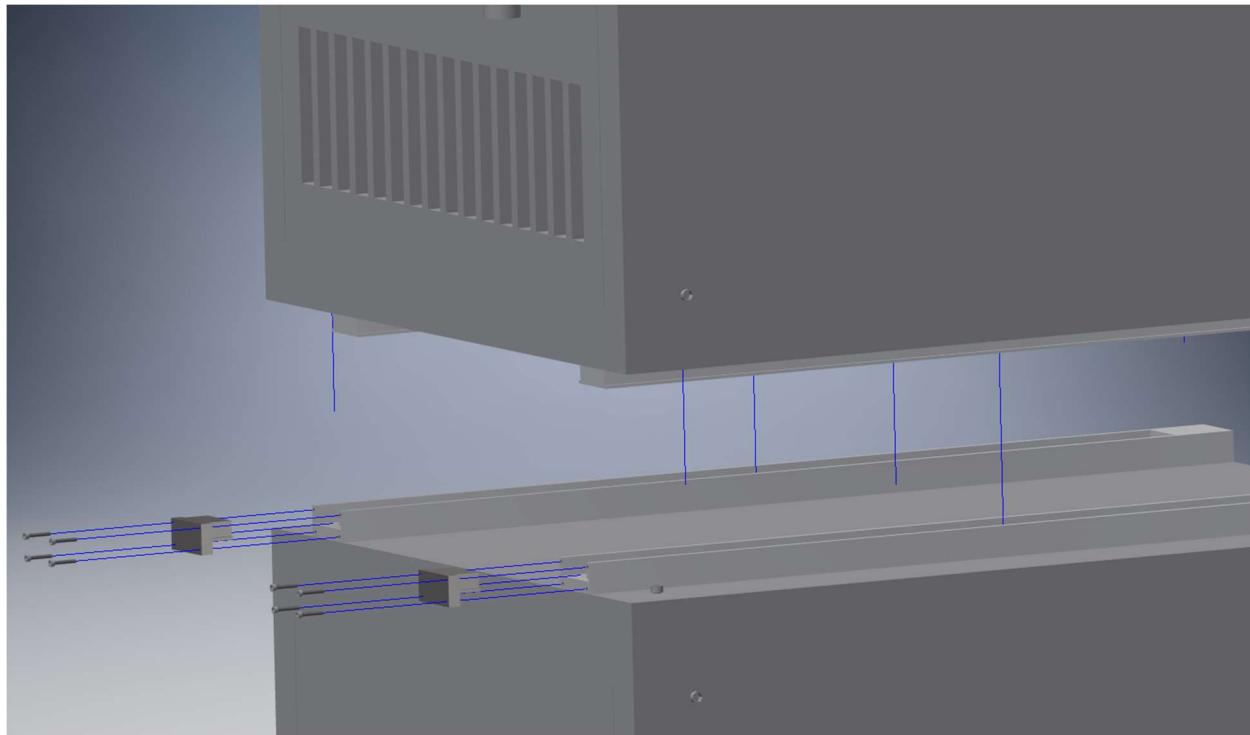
Vue éclatée de la superposition de deux coffrets avec le rail
